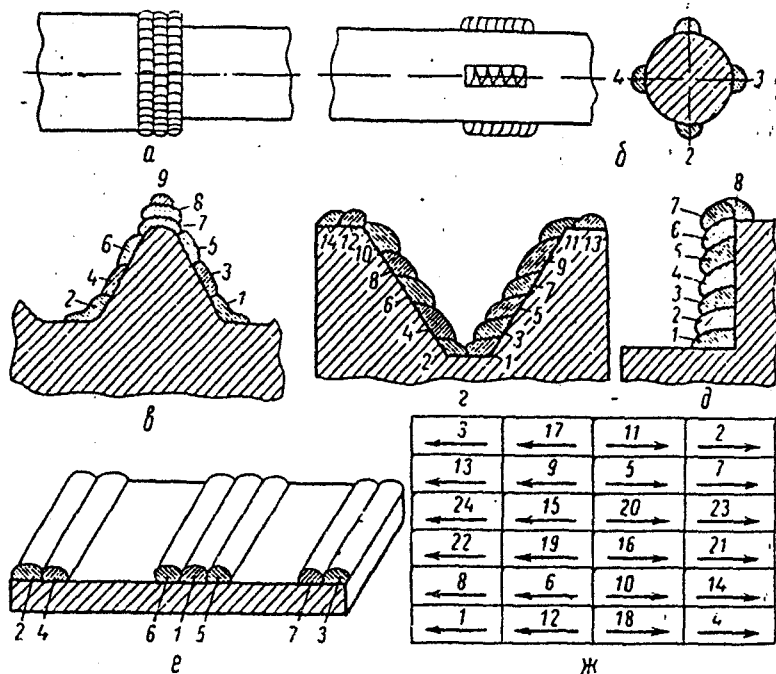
Порядок (обозначен цифрами) наложения валиков при наплавке:
